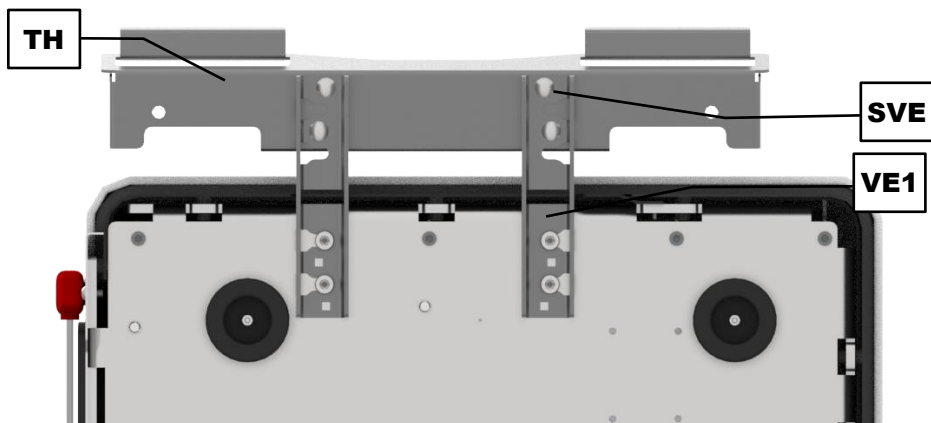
Смонтированное приспособление для транспортировки (вид снизу)
